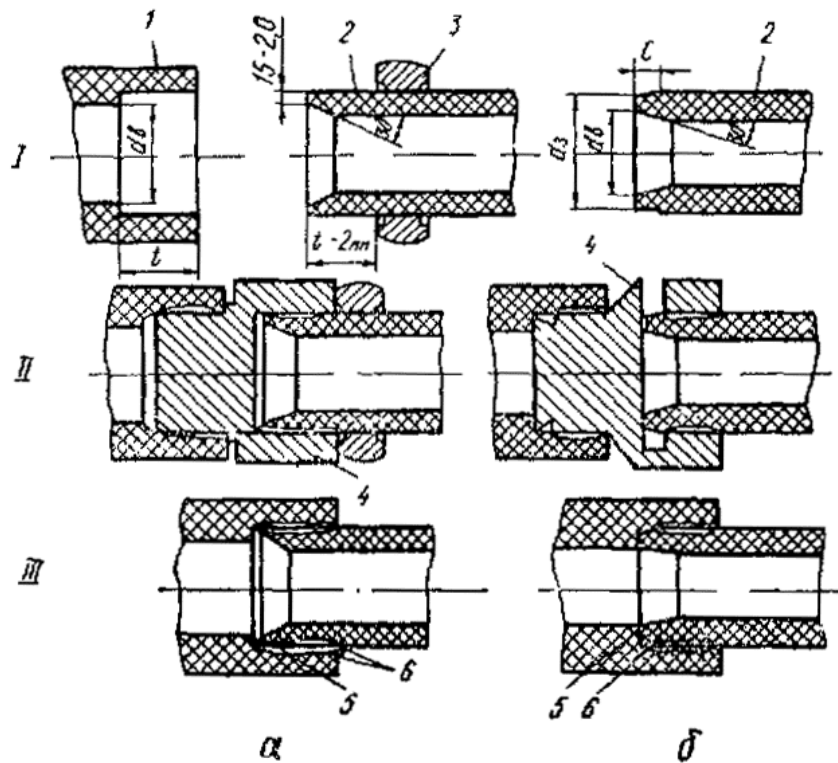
Последовательность процесса сварки труб внахлест:
